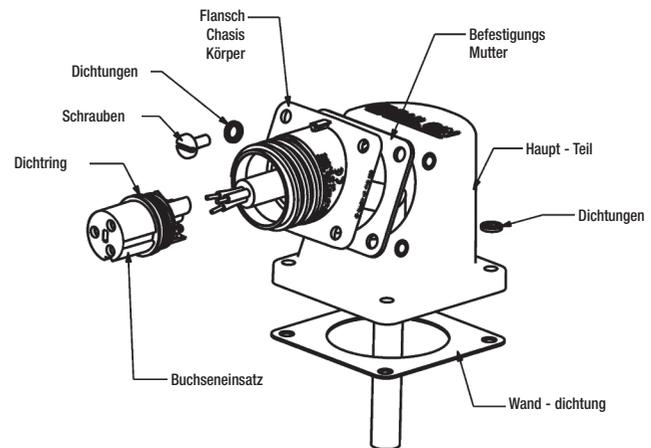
Befestigung Flansch/Wand (PX0941 & PX0950)
